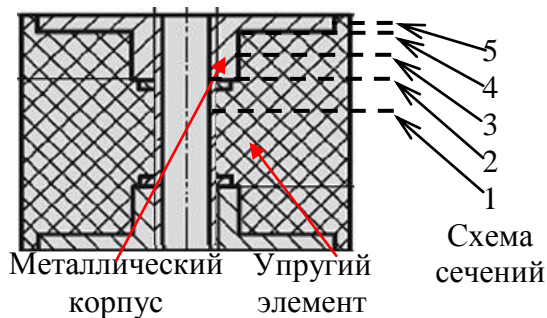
Резинометаллический амортизатор, тип С; схема рассматриваемых сечений
